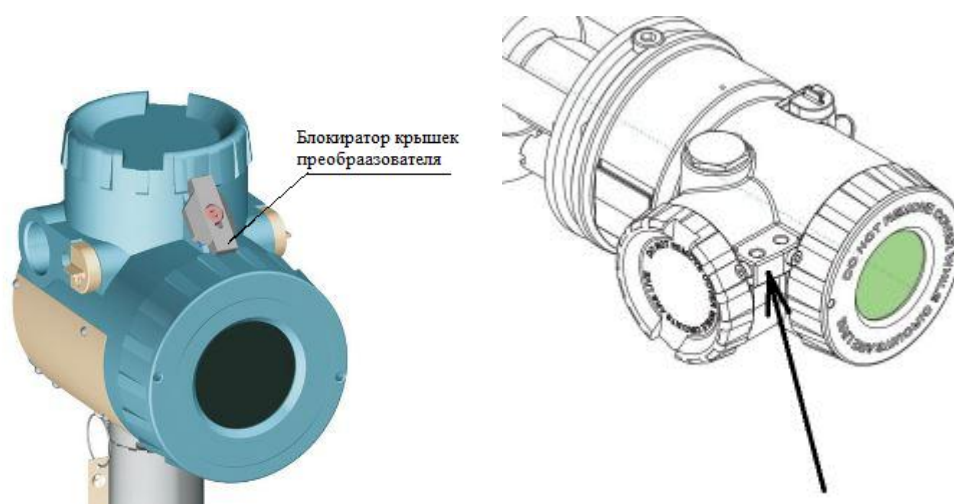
Схема установки блокиратора крышек корпуса преобразователя, пломбируемого наклейкой
